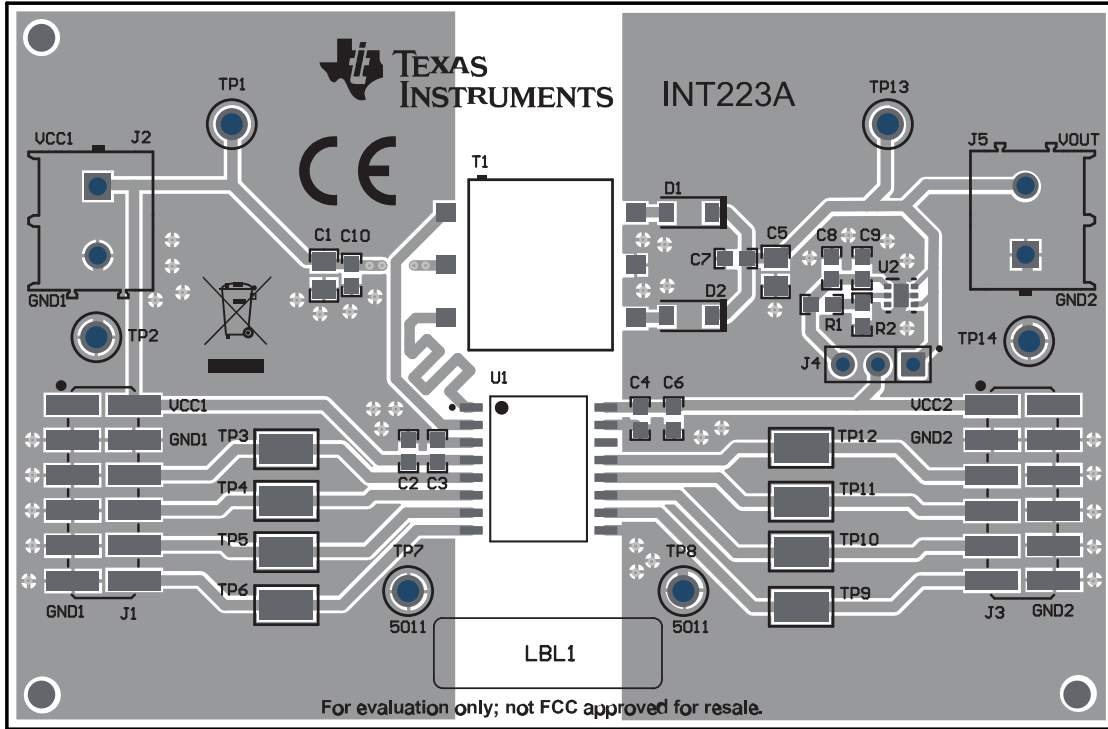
ISO7741TADWEVM PCB 布局 - 复合顶视图
